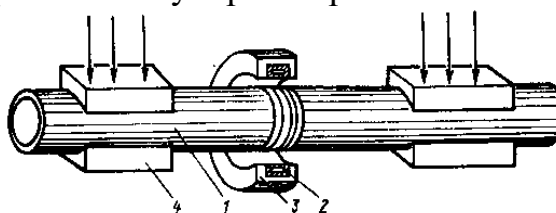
Схема высокочастотной сварки труб:
